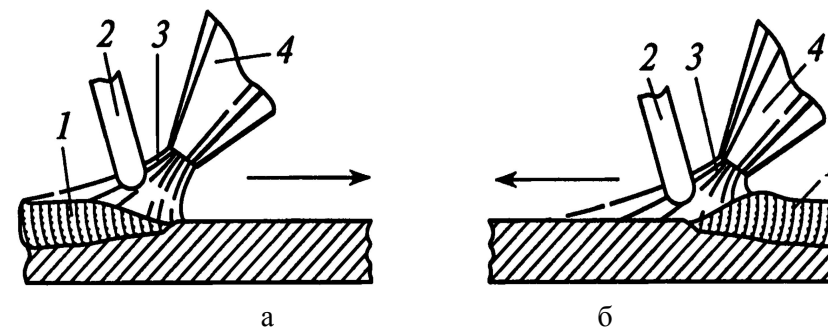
Основные способы газовой сварки: а – правый способ сварки; б – левый способ сварки; 1 – формирующий шов; 2 – присадочный пруток; 3 – пламя горелки; 4 – горелка
